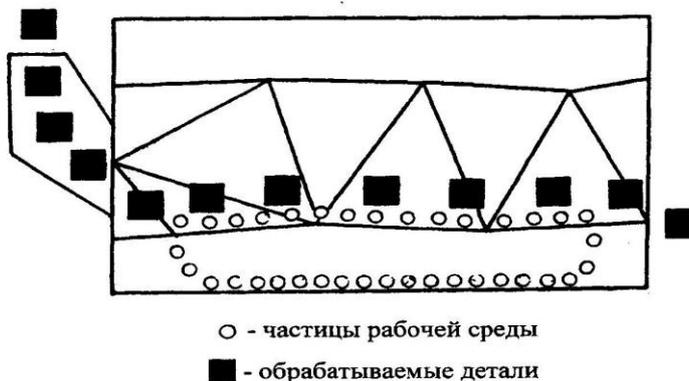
Схема движения деталей и частиц рабочих сред в станке для отделочно-зачистной и упрочняющей обработки деталей
